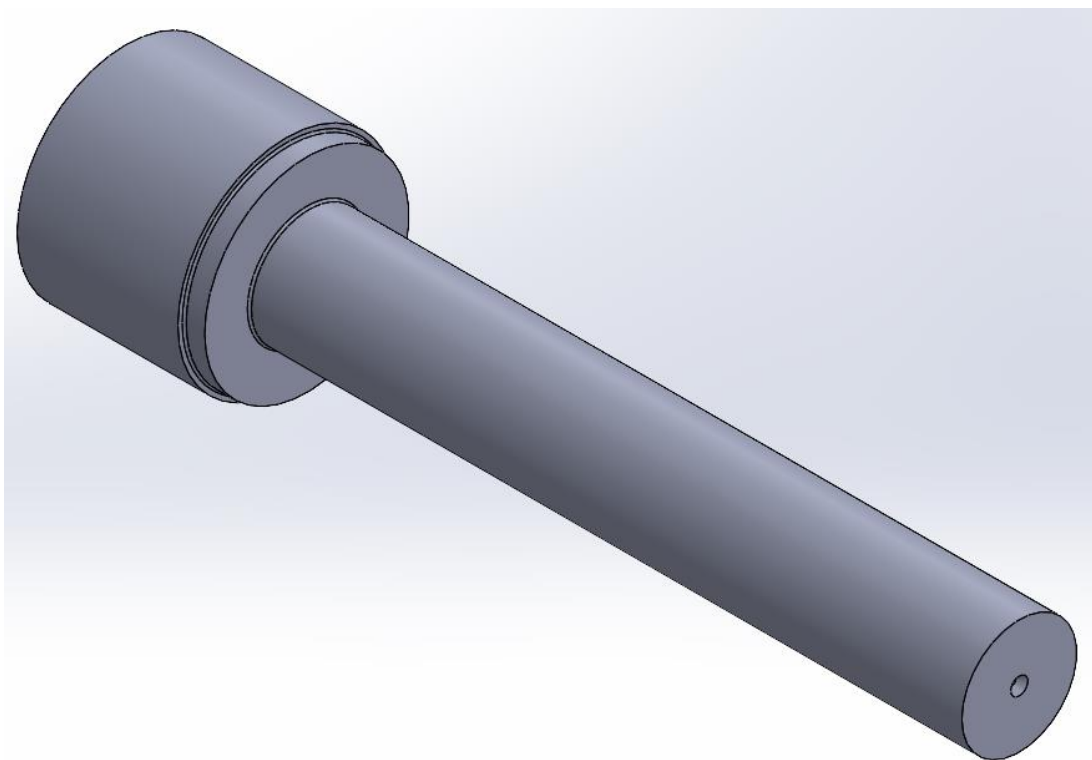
Заготовка для обробки деталі на операції 030
